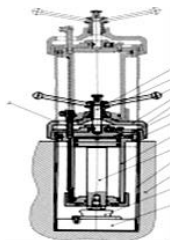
Приспособление для выпрессовки гильзы из блока цилиндров
